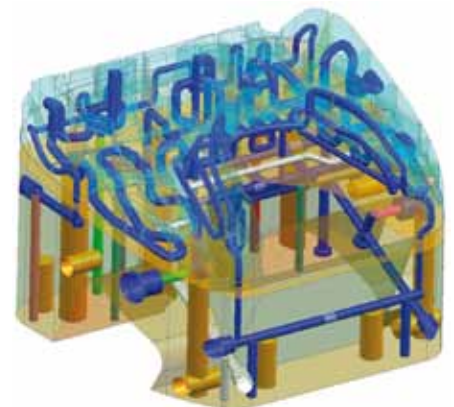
Werkzeugformeinsatz innenliegender Kühlkanäle (Quelle: ConceptLaser)
